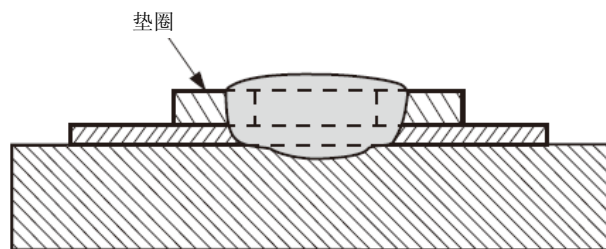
B — 使用垫圈的电弧点焊缝
